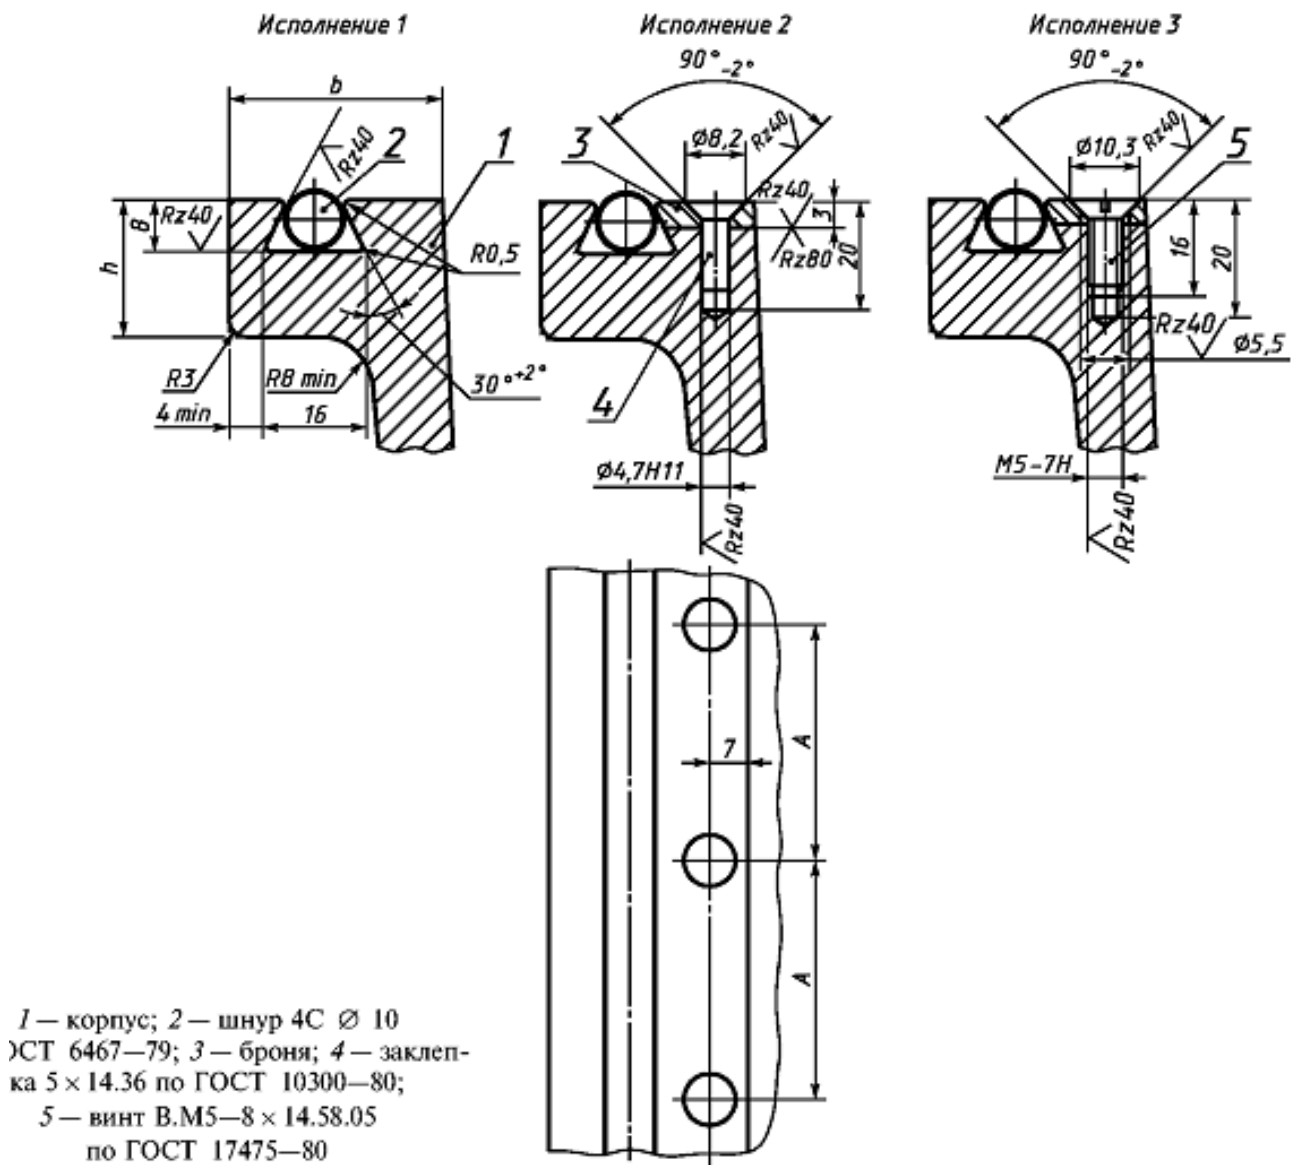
Конструкции паза под резиновый уплотнитель:
